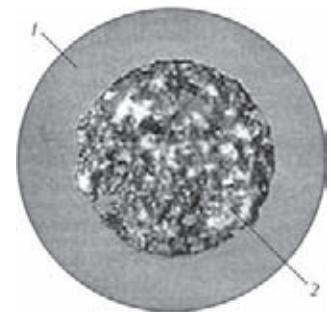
Порошковый присадочный пруток TG-X в разрезе: 1 — оболочка из нержавеющей стали; 2 — флюс
